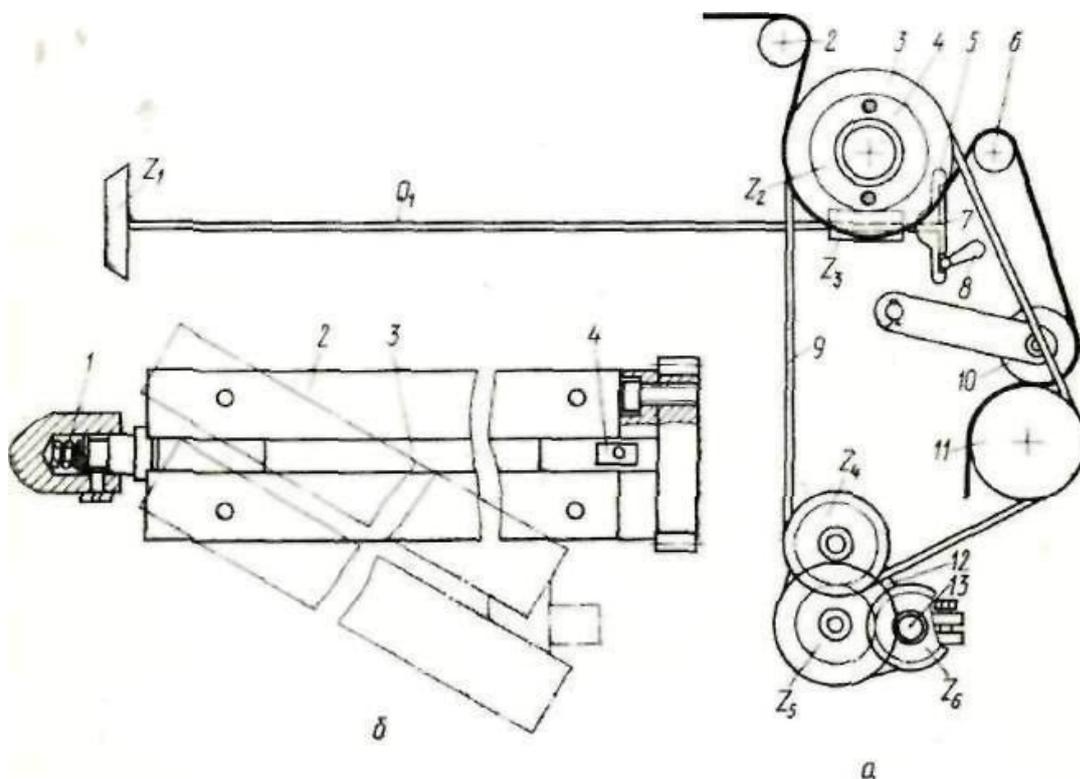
Механизм движения ткани станка: а-товарный регулятор; б -товарный валик.
